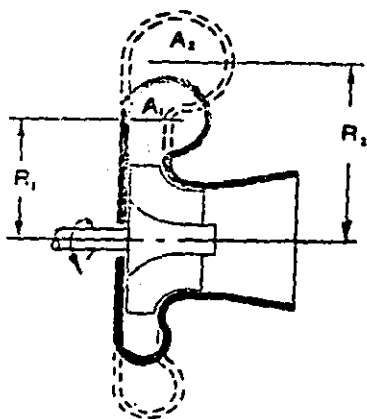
Carcasa de turbina sin paletas con diferentes medidas de R.
